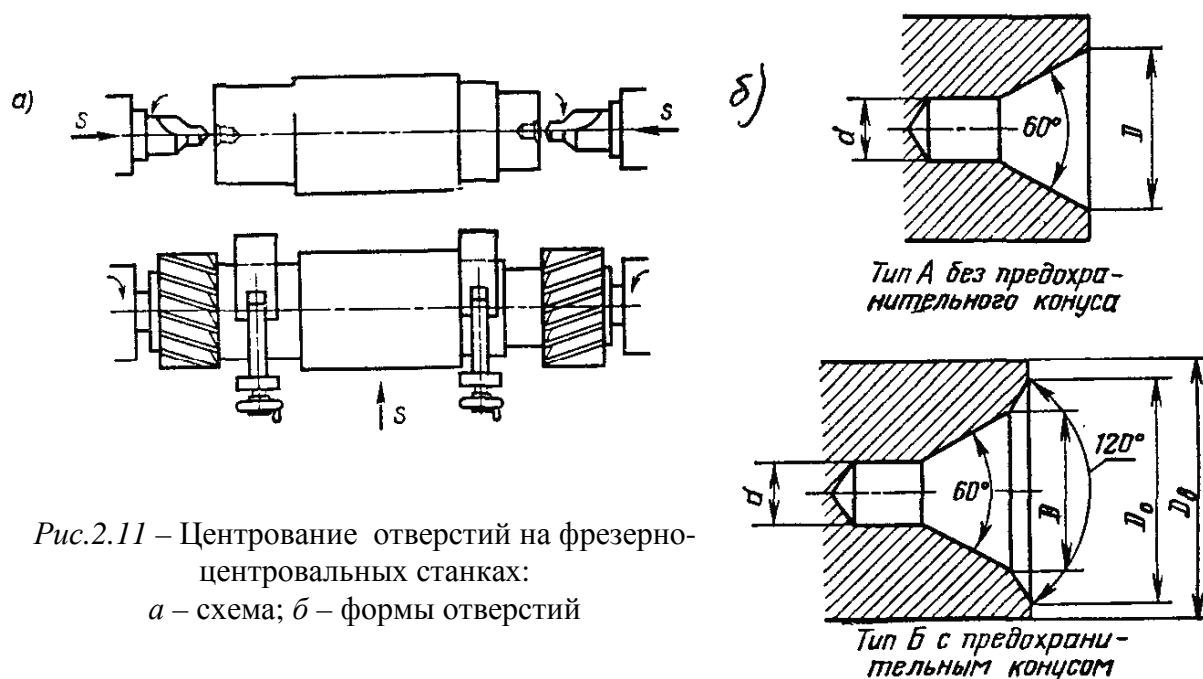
Центрование отверстий на фрезерно-центровальных станках:
